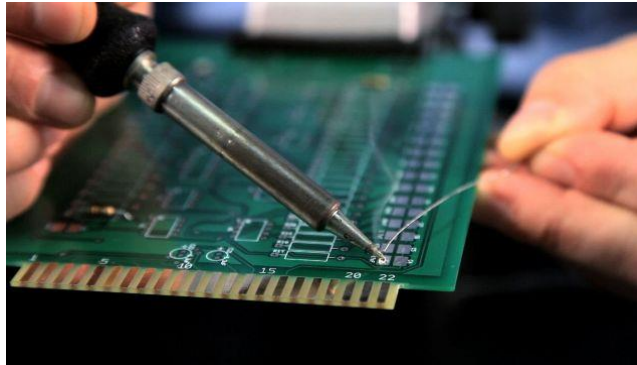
Soldadura Blanda Empleada en un Circuito Electrónico
